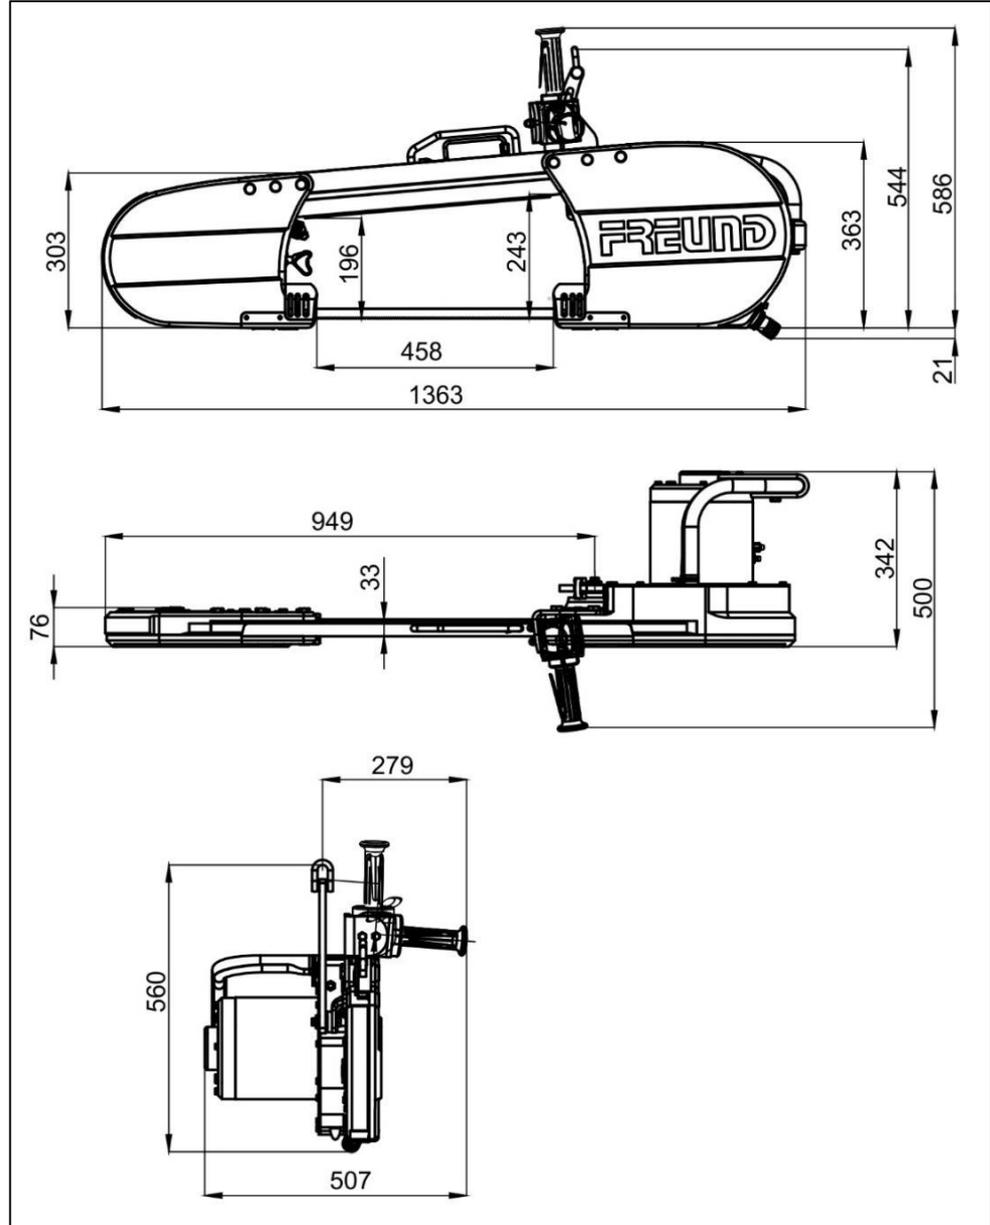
Dimensiones de la sierra de cinta de esquinado [datos en mm)
